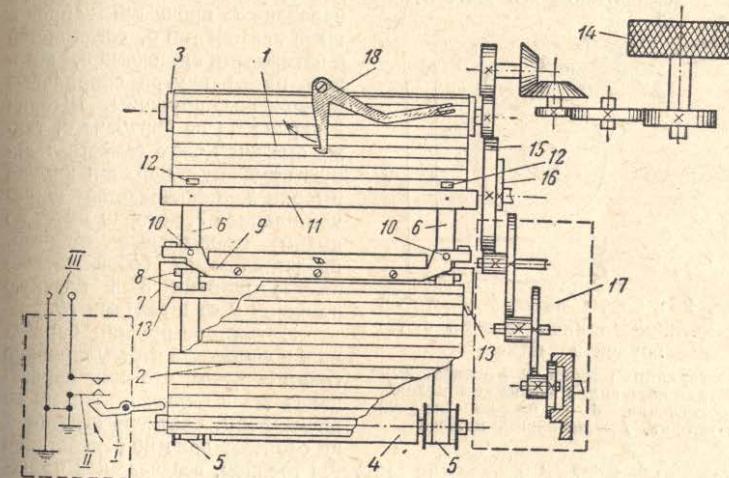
Схемы действия механизма шторок затвора фотоаппарата «Киев» и синхроустройства (см. стр. 35).
